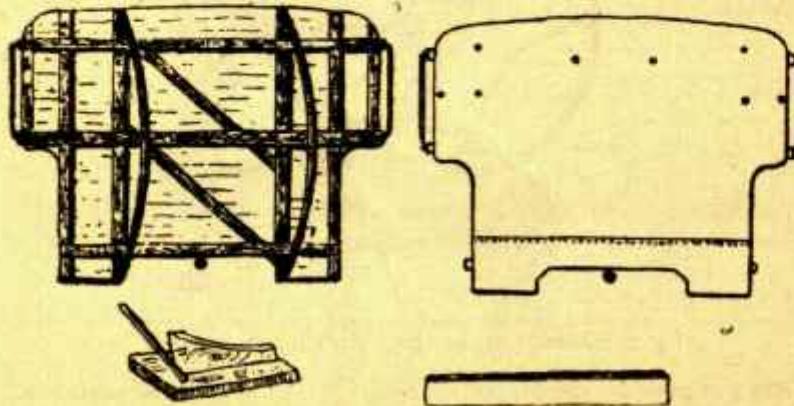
a 4.—Mesa vista por debajo y por su plano. Detalle de una cala y del estribo.
